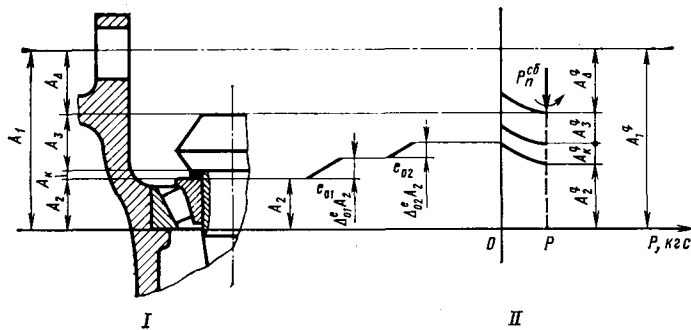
Схема образования технологической сборочной размерной цепи на положение ведущей шестерни главной передачи: I — конструкторская цепь; II — технологическая цепь
